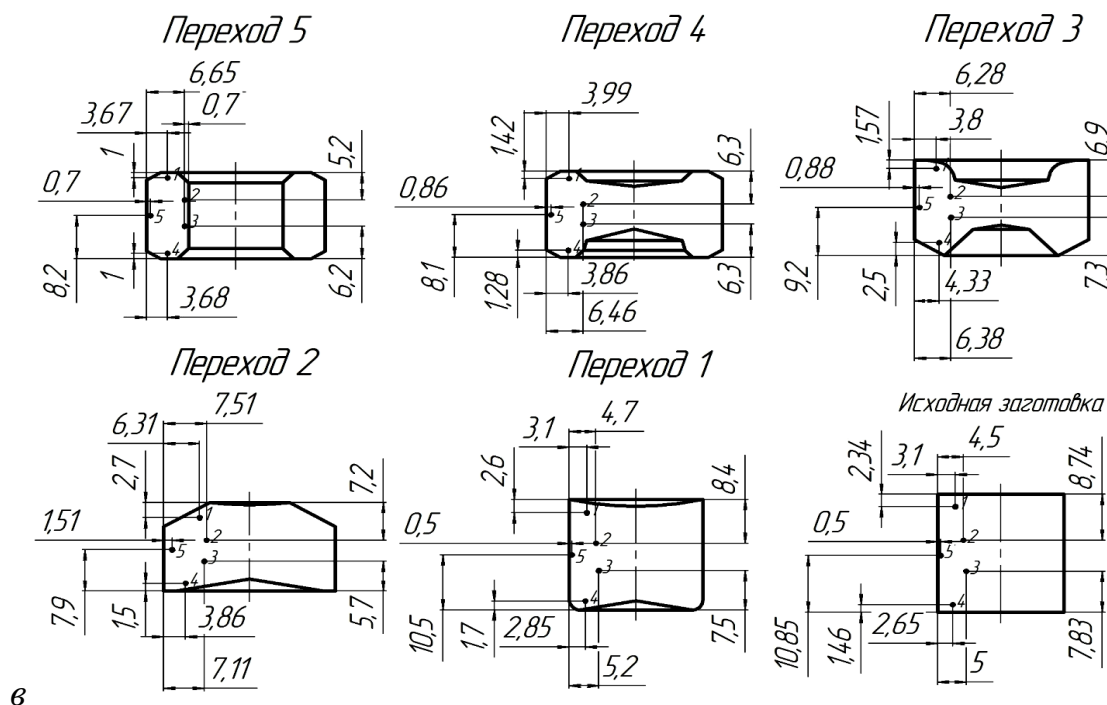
Переходы деформирования: 1 – осадка заготовки; 2 - осадка с подформовкой; 3 - формовка предварительная, 4 - формовка окончательная; 5 – пробивка отверстия; (цифры – координаты исследуемых зон на продольных шлифах заготовок)
